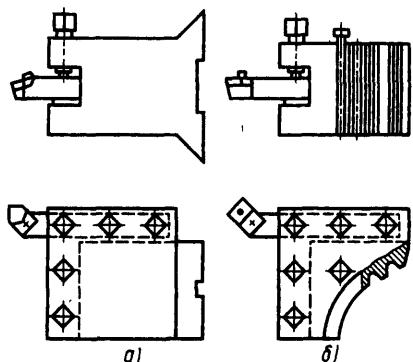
Резцовые блоки без предварительной настройки на размер (*а*, *б*)
